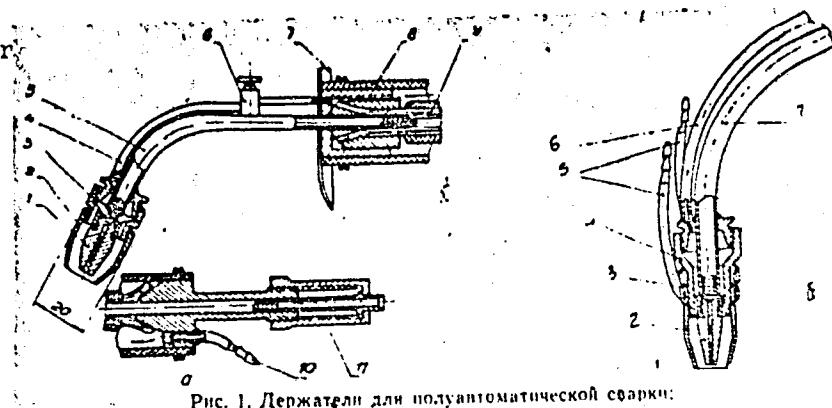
Держатели для полуавтоматической сварки:
